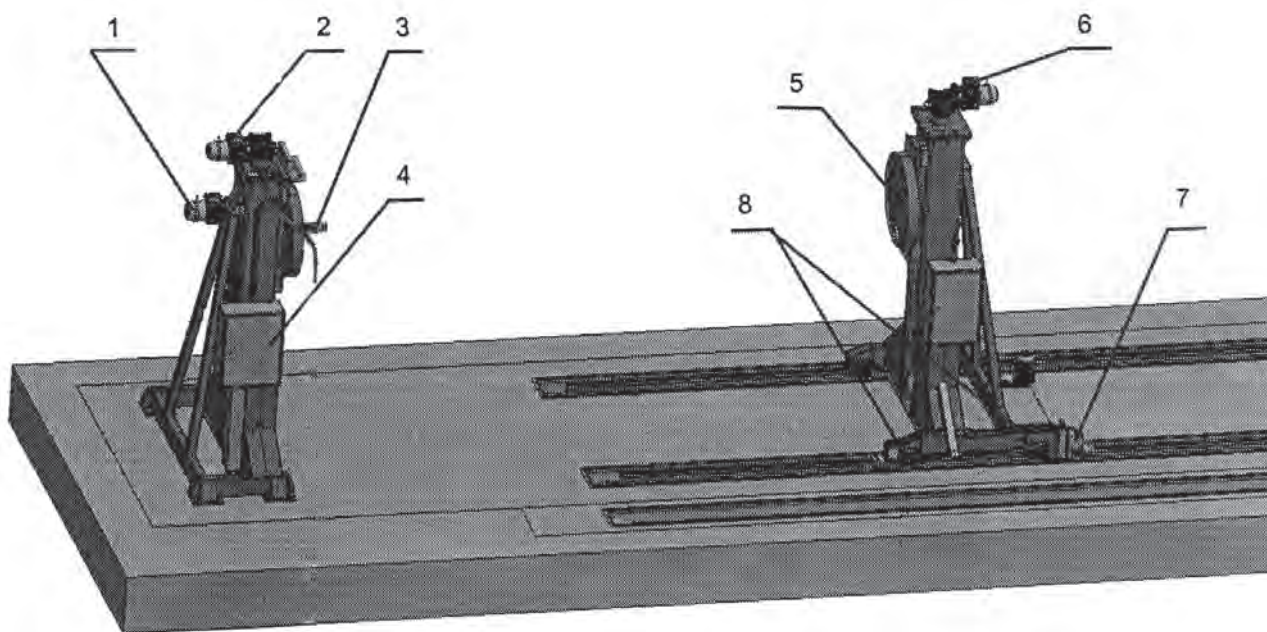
Внешний вид кантователя грузоподъемностью 10 т: 1 – привод поворотного механизма; 2 – привод вертикального перемещения поворотного механизма неподвижной колонны; 3 – ведущий поворотный механизм; 4 – пульт управления; 5 – ведомый поворотный механизм; 6 – привод вертикального перемещения поворотного механизма подвижной колонны; 7 – механизм фиксации колонны; 8 – ролики
